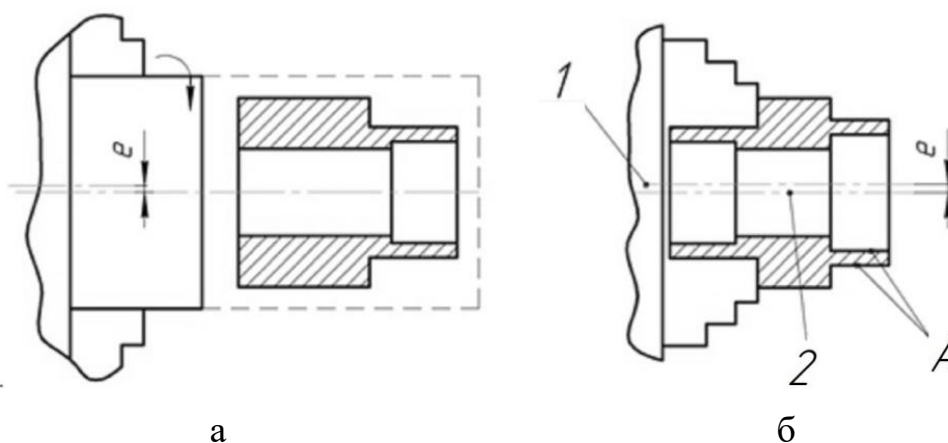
Схемы передачи смещения установочно-зажимных элементов приспособления обработанной детали
